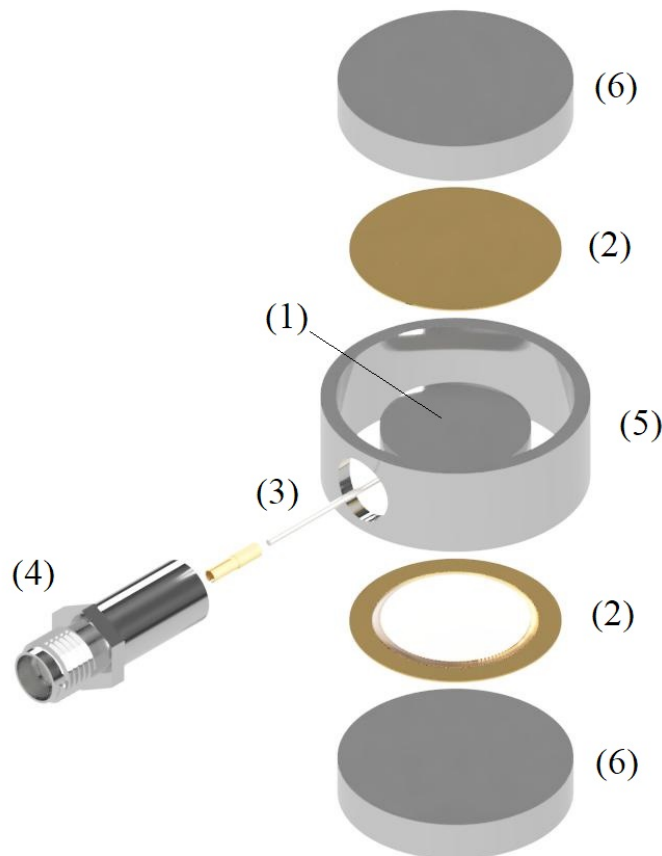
Perspectiva explodida do sensor de força uniaxial. Fonte: Autor.
